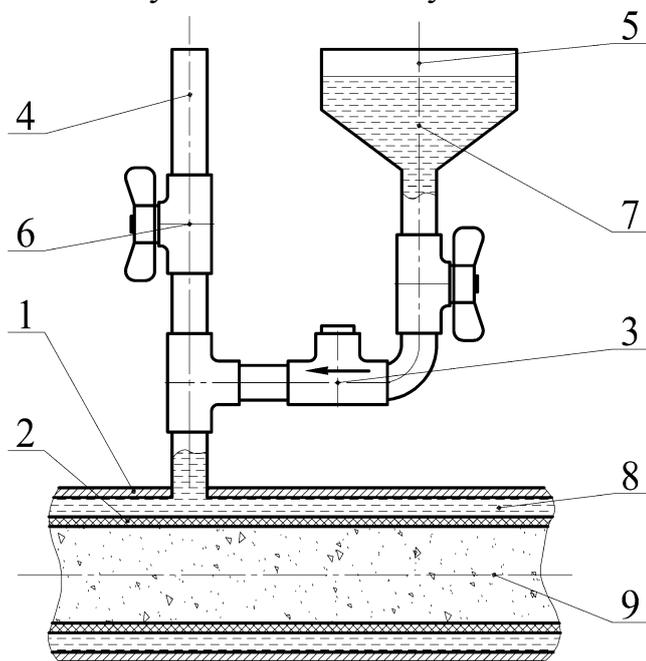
Пристрій для автоматичного поповнення робочої рідини: 1 – корпус гідравлічного компенсатора; 2 – трубчаста гумотканинна діафрагма; 3 – зворотний клапан; 4 – трубка для випуску повітря; 5 – місткість для робочої рідини; 6, 7 – шарові крани; 8 – робоча камера компенсатора; 9 – магістраль із розчинною сумішшю
